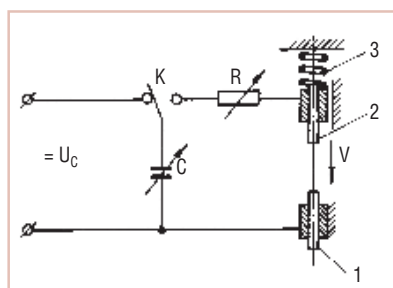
Схема процесса УКС: 1 — неподвижная деталь; 2 — деталь, движущаяся со скоростью  $V$ ; 3 — приводная пружина;  $U_C$  — напряжение зарядки конденсаторов;  $C$  — конденсаторы;  $K$  — ключ, переключающий конденсаторы с зарядки на разряд;  $R$  — резистор, управляющий характеристиками процесса
